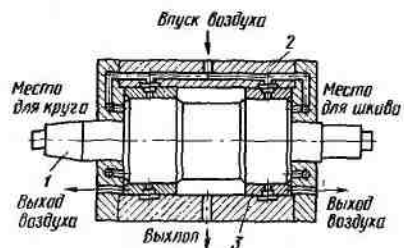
Конструкция аэростатического подшипника круглошлифовального станка
